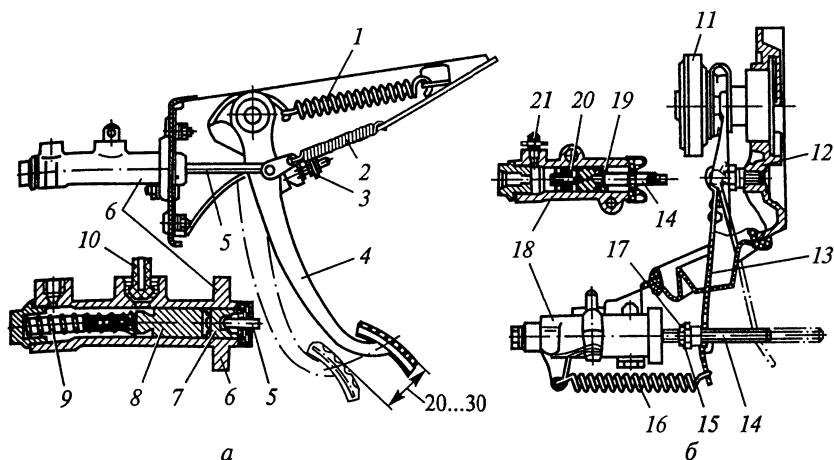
Привод сцепления легковых автомобилей ВАЗ:
